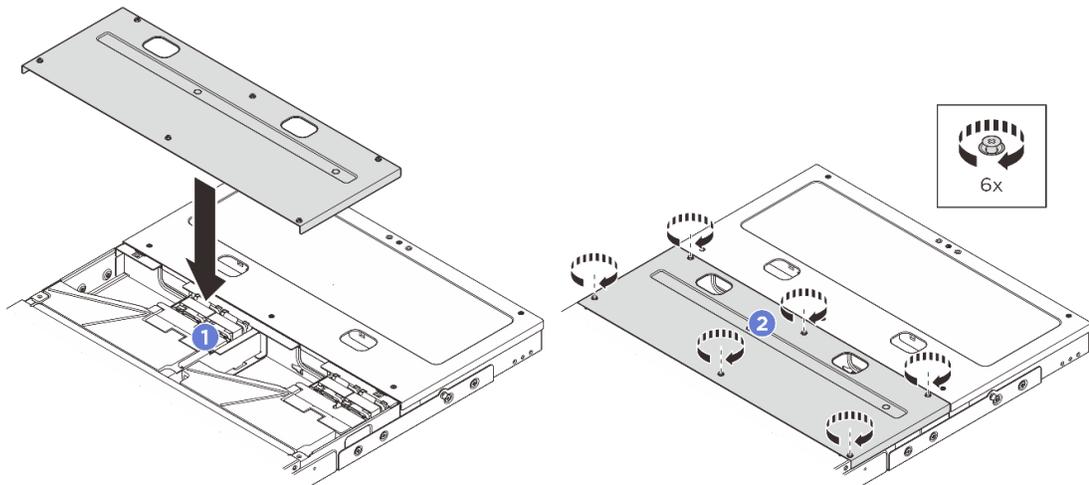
Установка среднего верхнего кожуха корпуса 1U2N
